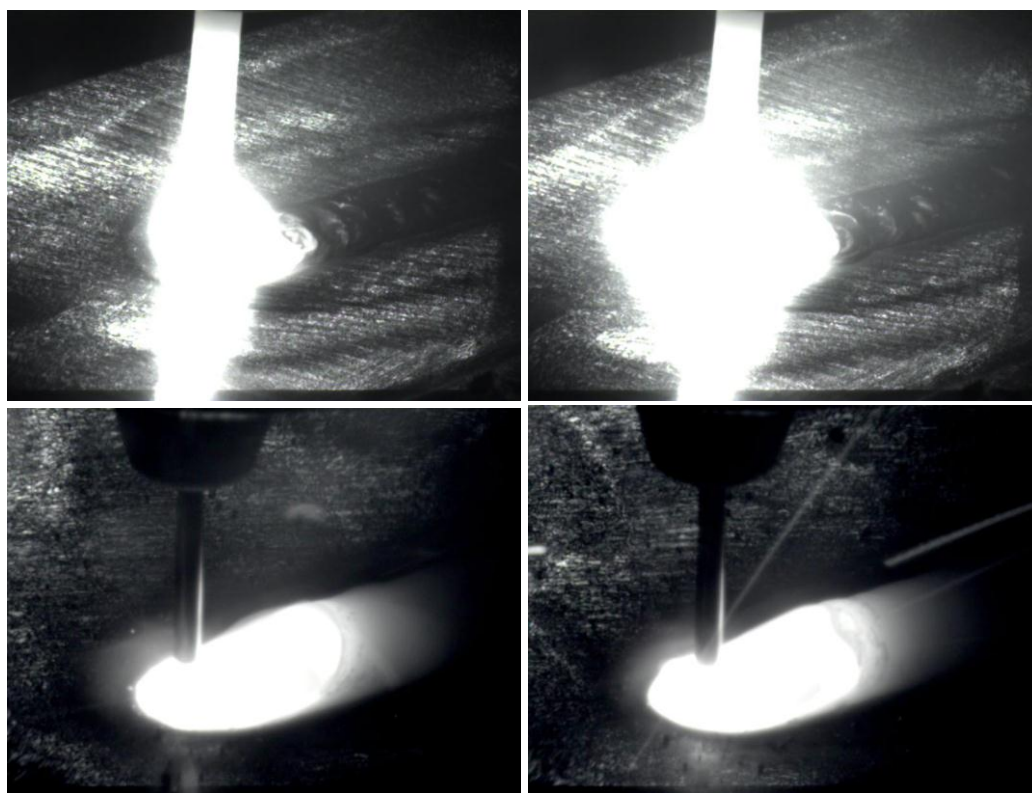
Imagens obtidas pelo sistema de visão “Viasolda” em soldagens TIG (cima) e MAG (baixo) (MOTA, 2011; MOTA *et al.*, 2011)
